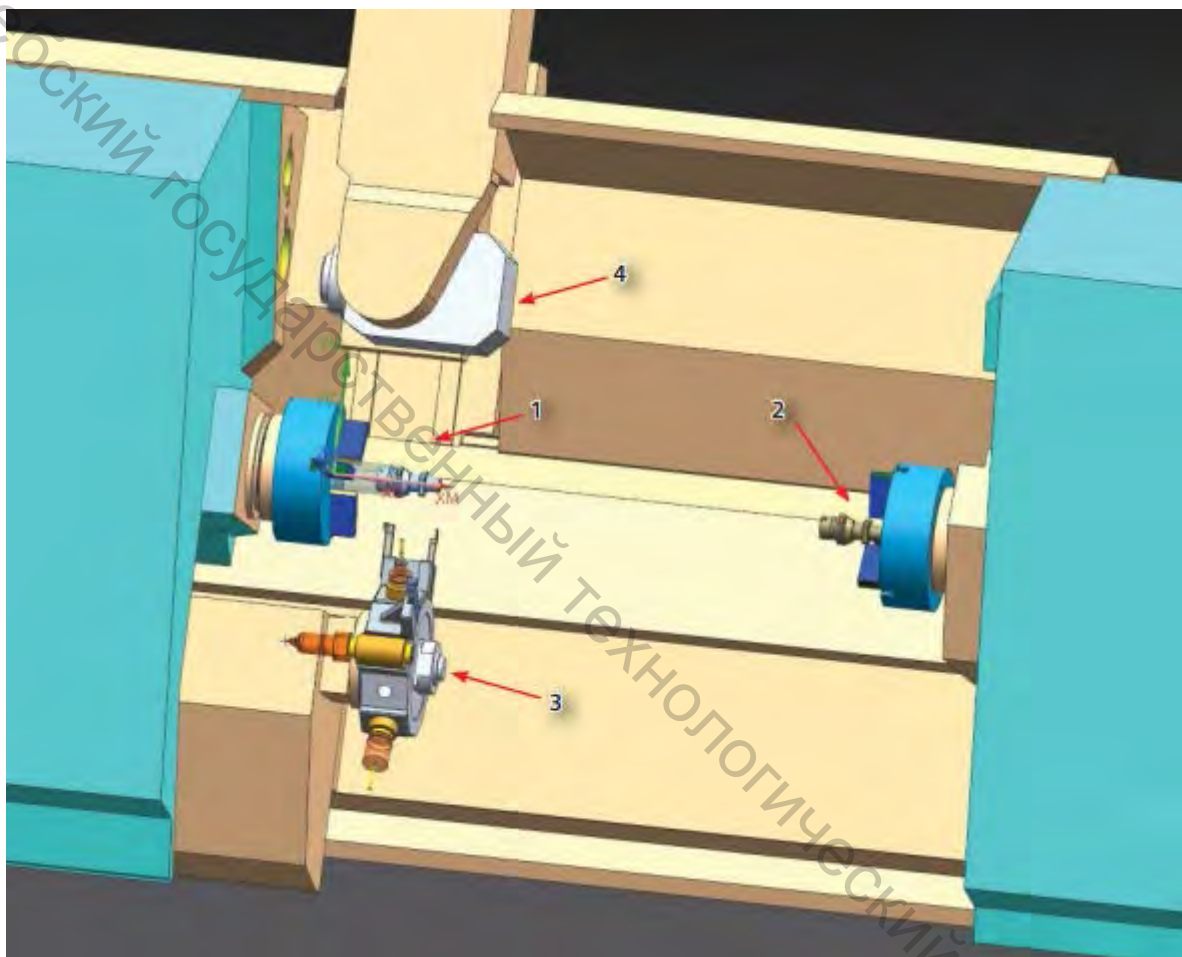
Схема токарно-фрезерного станка с револьверной головкой и поворотным шпинделем:
